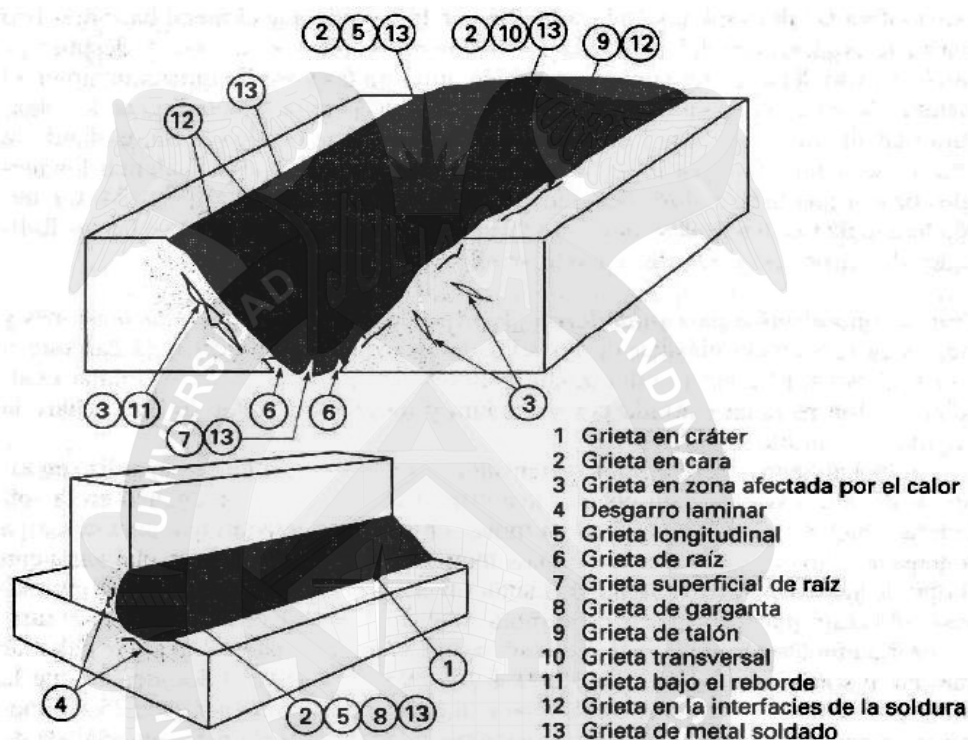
Las grietas en las soldaduras tienen múltiples causal.
